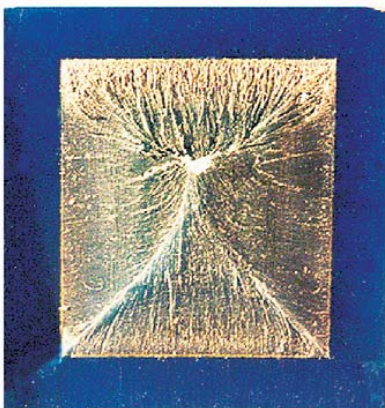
Bruchfläche einer FNCT-Probe aus einem PE-100-Rohr.
